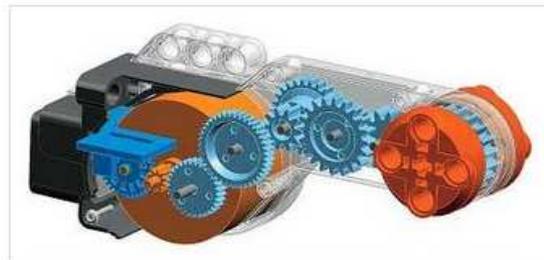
Figura del sistema de engranajes internos del servomotor
